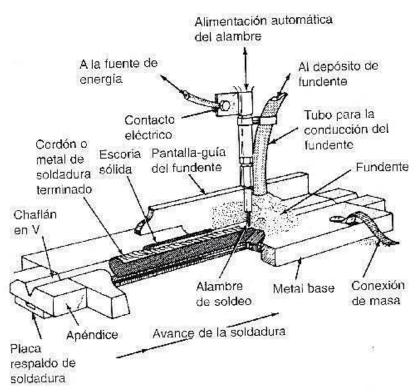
Esquema del proceso de soldadura SAW
